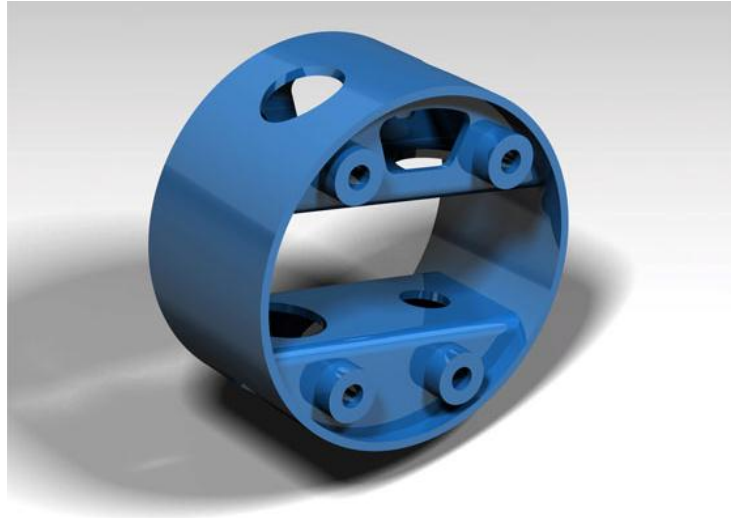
Muestra de uno de los bujes desechados. Este diseño estaba planteado para ser fabricado en hierro, partiendo de un tubo de grandes dimensiones y dos planchas cortadas por láser, dobladas y soldadas al tubo.
